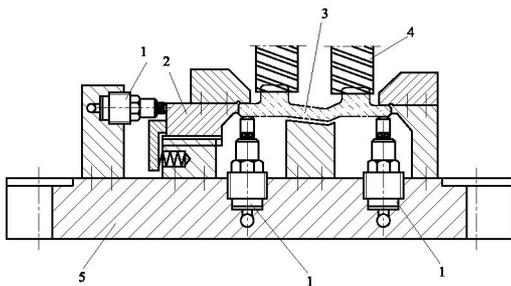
Fräsvorrichtung hydraulisch betätigt
